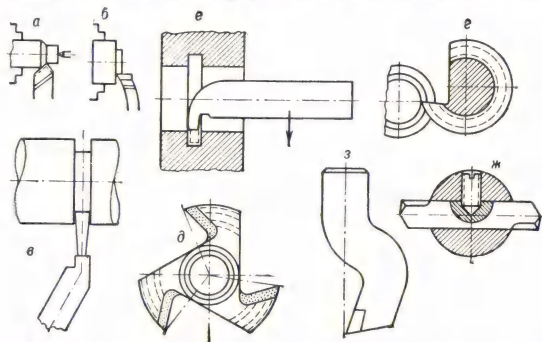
Некоторые типы резцов: а — токарный проходной прямой; б — токарный подрезной отогнутый; в — токарный прорезной отогнутый; г — токарный круглый; д — токарный фасонный твердосплавный; е — расточный для внутренних канавок; ж — расточный двухлезвийный; з — строгальный подрезной.
